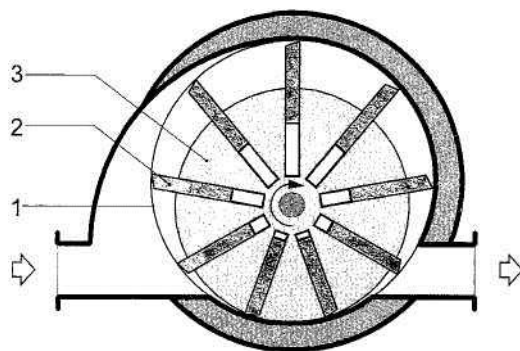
Пластинчастий (шиберний) компресор:
